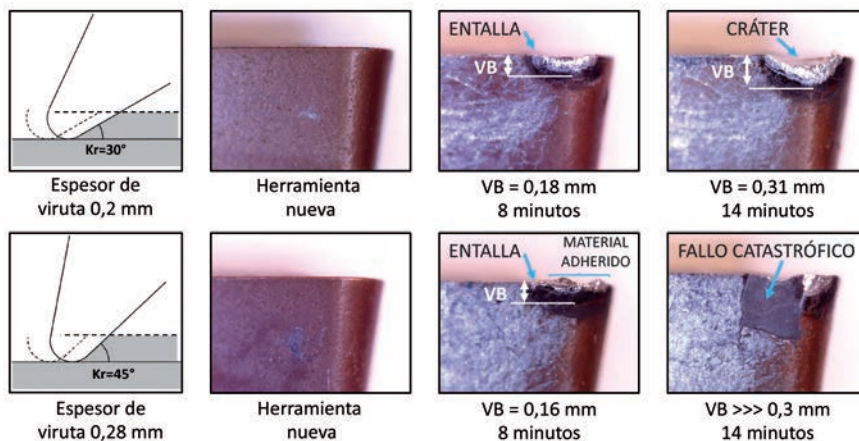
Torneado de Inconel 718 con herramienta de alto avance V_c 50 m/min, f 0,4 mm/rev, a_p 0,5 mm. Mismas condiciones con distinto ángulo de ataque (K) 30° y 45°. El mayor espesor de viruta en el segundo caso (abajo) ocasiona la rotura del filo (desgaste según norma ISO 3685-1993).
